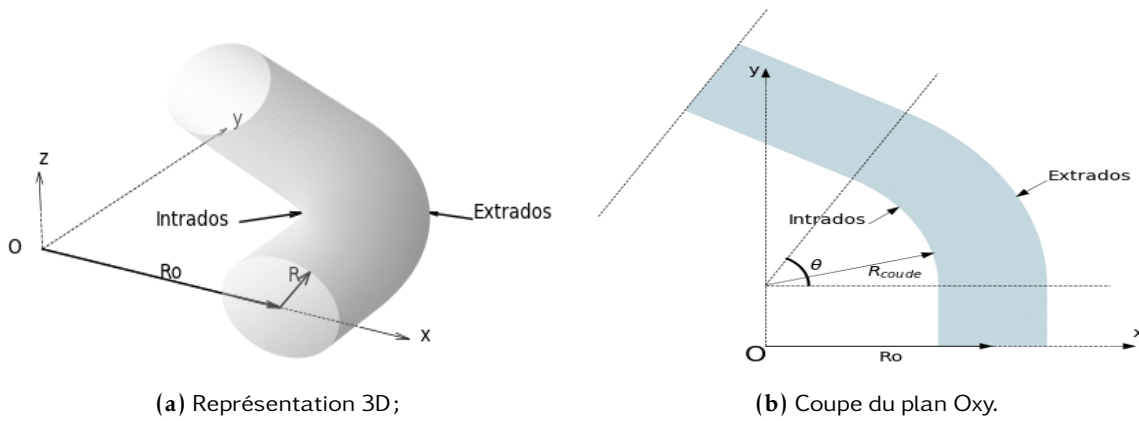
Paramètres utilisés pour définir un tube coudé.
